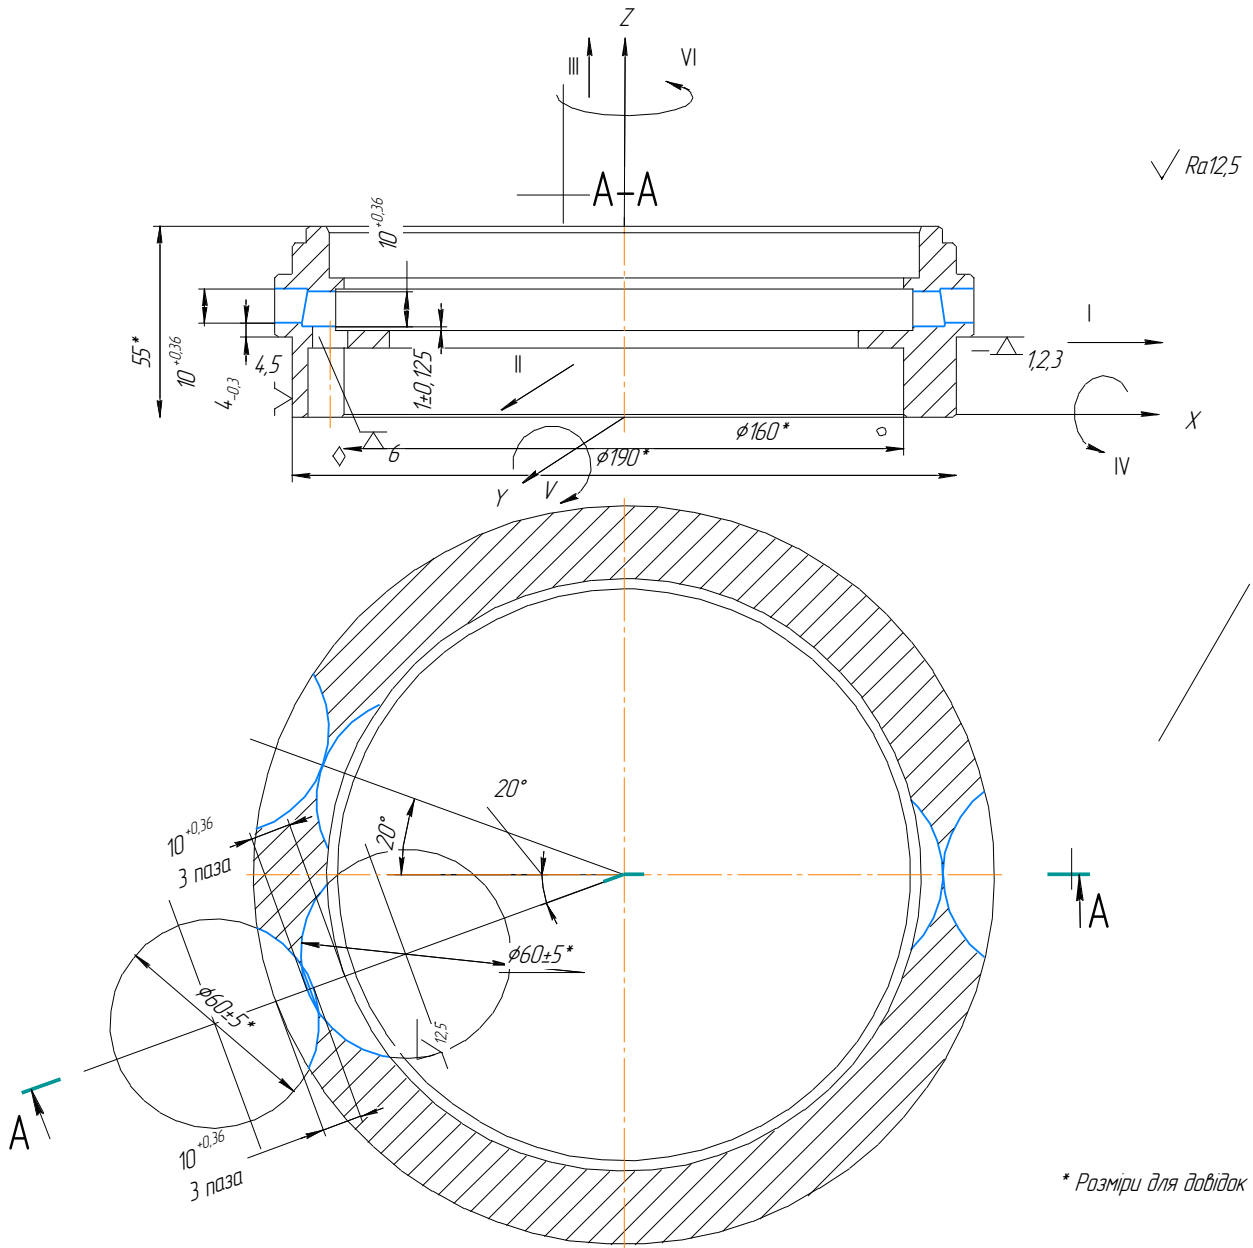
Схема базування деталі на фрезерній операції
